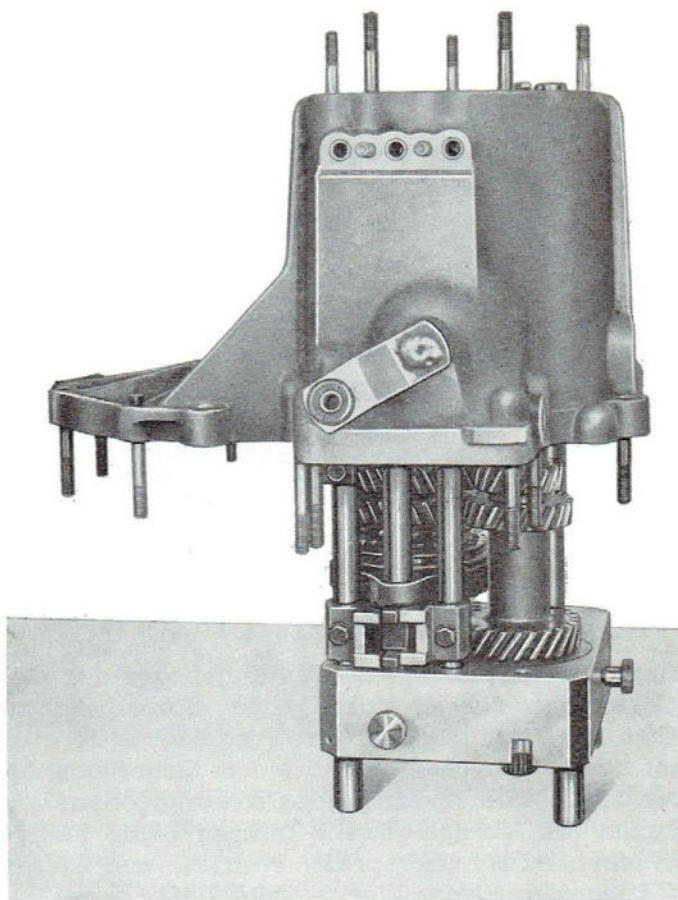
Aufschieben des Getriebegehäuses auf das Werkzeug A. 70105 mit vormontiertem Getriebe.
